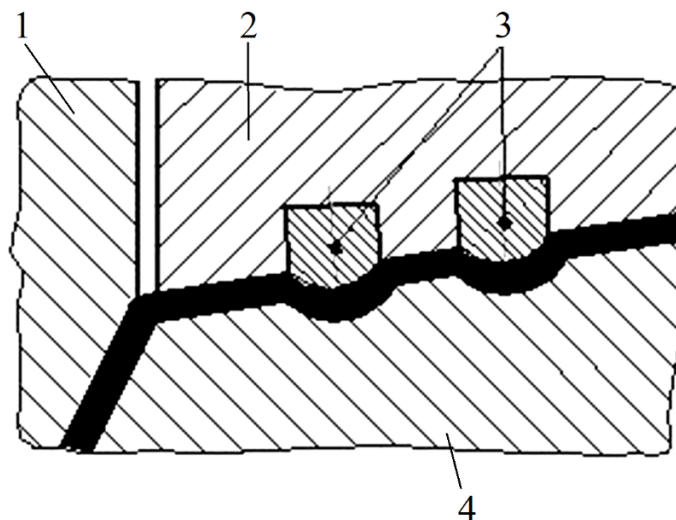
Схема встановлення перетяжних ребер штампа:
